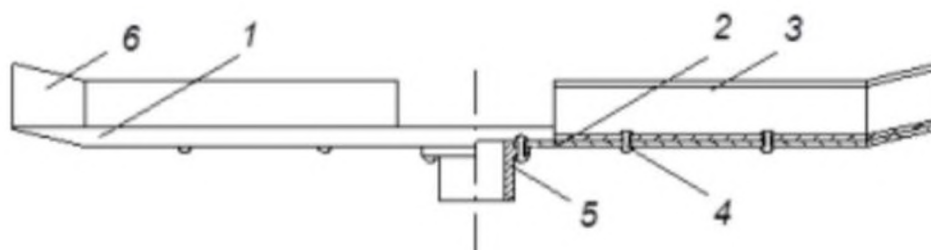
Схема відцентрового туковисівного робочого органу із плоским диском з конусною обичайкою: 1 – зона конусної обичайки; 2 - плоский диск; 3 – лопатка; 4 – заклепкове з'єднання; 5 - маточина; 6 - подовжувач лопатки
